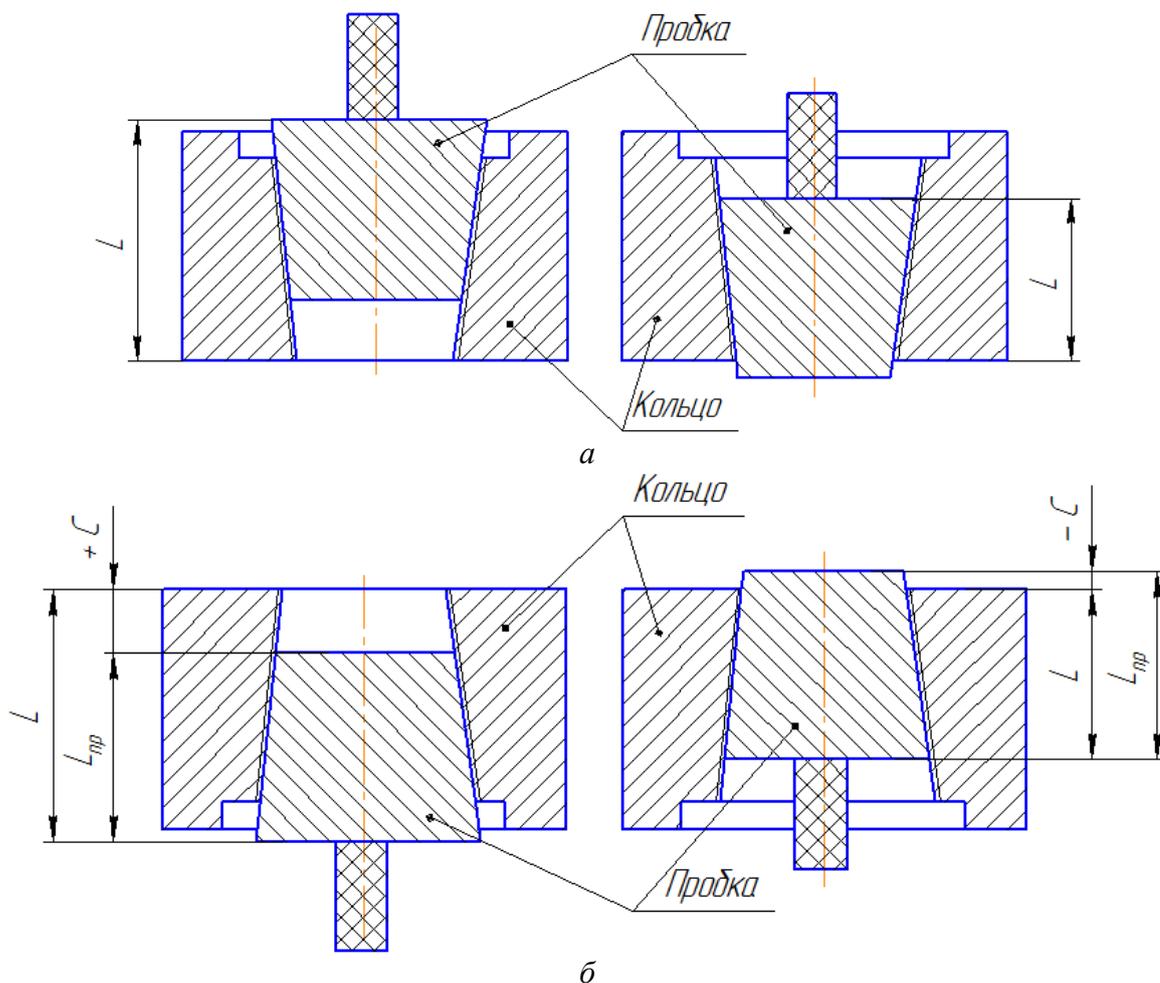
Схемы припасовки гладкого контрольного калибра-пробки и гладкого или резьбового рабочего калибра-кольца
